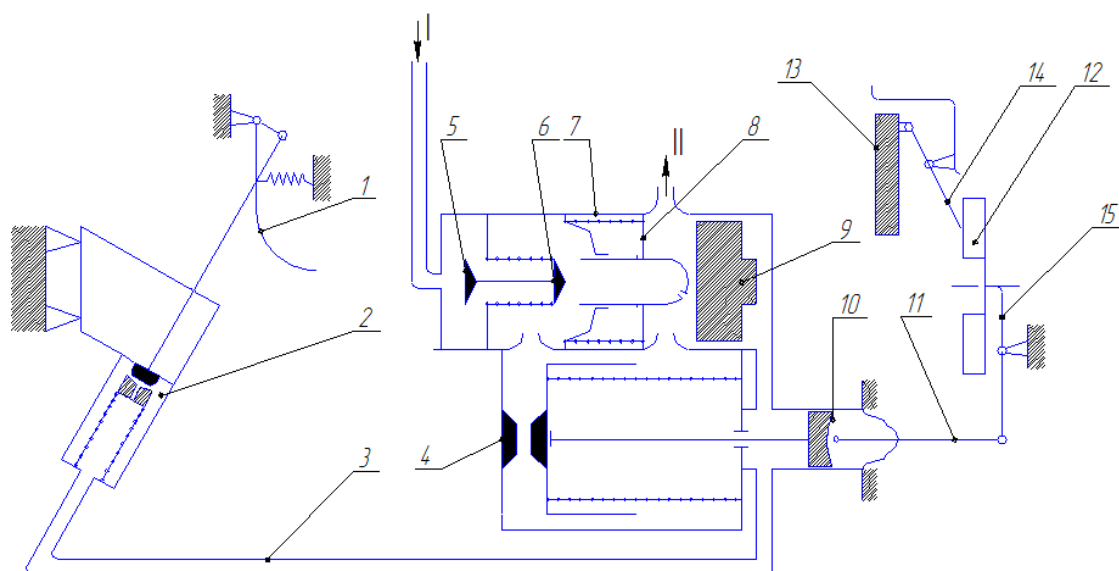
Существующая схема привода сцепления автомобиля КамАЗ: 1 - педальный привод; 2 - главный гидроцилиндр; 3 - гидролиния; 4 - силовой гидроцилиндр; 5 - клапан сжатого воздуха; 6 - атмосферный клапан; 7 - картер мембранного устройства; 8 - мембрана; 9 - следящий клапан; 10 - гидравлический цилиндр выключения сцепления; 11 - шток; 12 - выжимной подшипник; 13 - нажимной диск; 14 - отжимной рычаг; 15 - вилка выключения сцепления.
